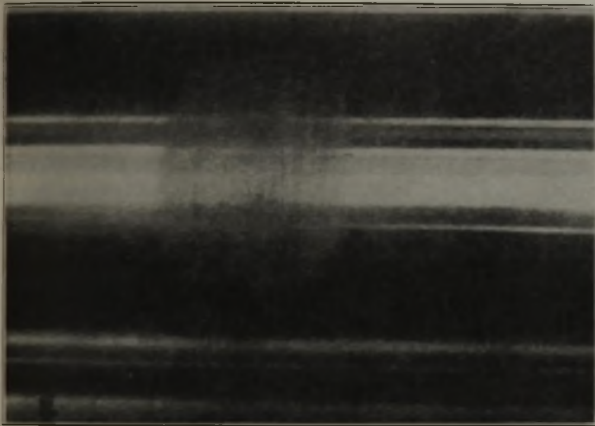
Durch gerutsches Band angelassene Oberfläche des Walzenballens mit haftengebliebenem Walzgut.
